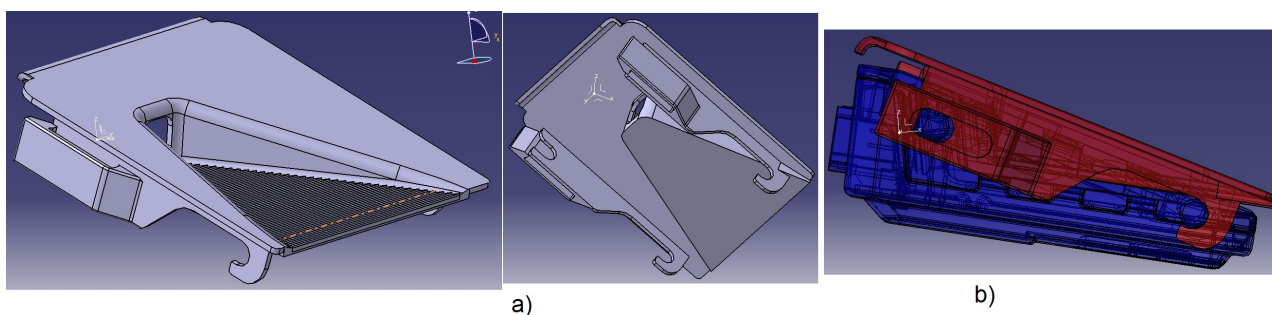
Varianta constructivă a II-a a bracketului (suportului) pentru camera video fixată pe parbrizul automobilului
